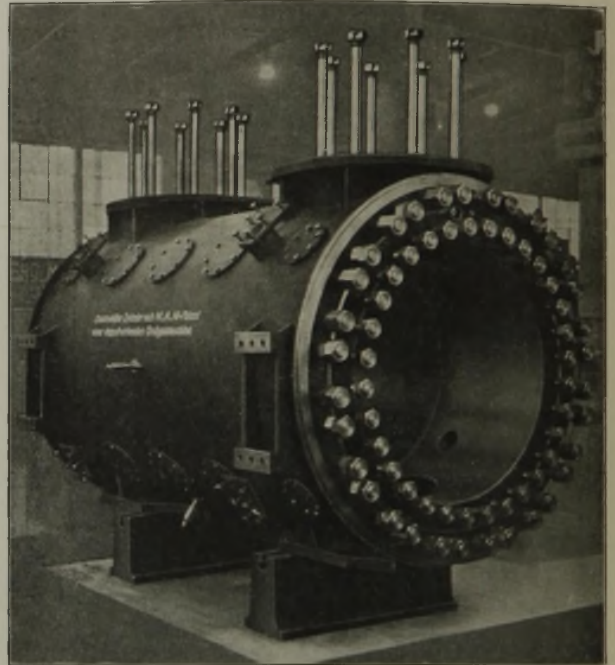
Einbaufertiger Gaszylinder aus Stahlblechen und Formstücken zusammengeschweißt.
